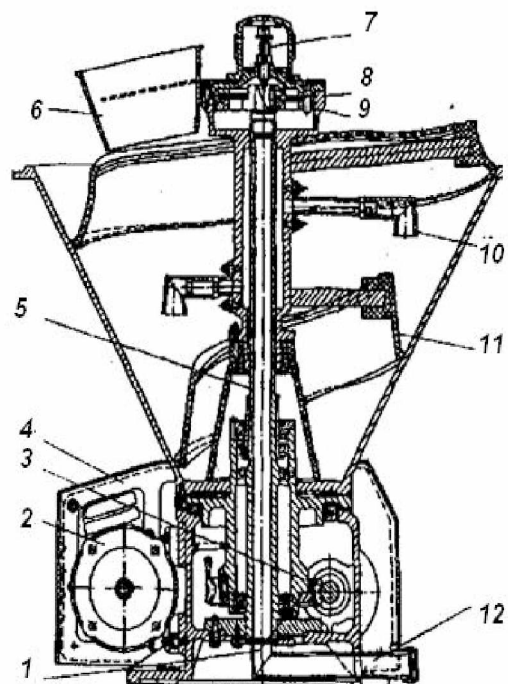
Тістоокруглювач Т1-ХТН: 1 - вал червяка; 2 - електродвигун; 3 - редуктор; 4 - корпус; 5 - вал, на якому закріплена спіраль; 6 - приймальна воронка; 7 - гвинт; 8 - диск; 9 - пальці; 10 - патрубки; 11 - формувальна спіраль; 12 - труба.
